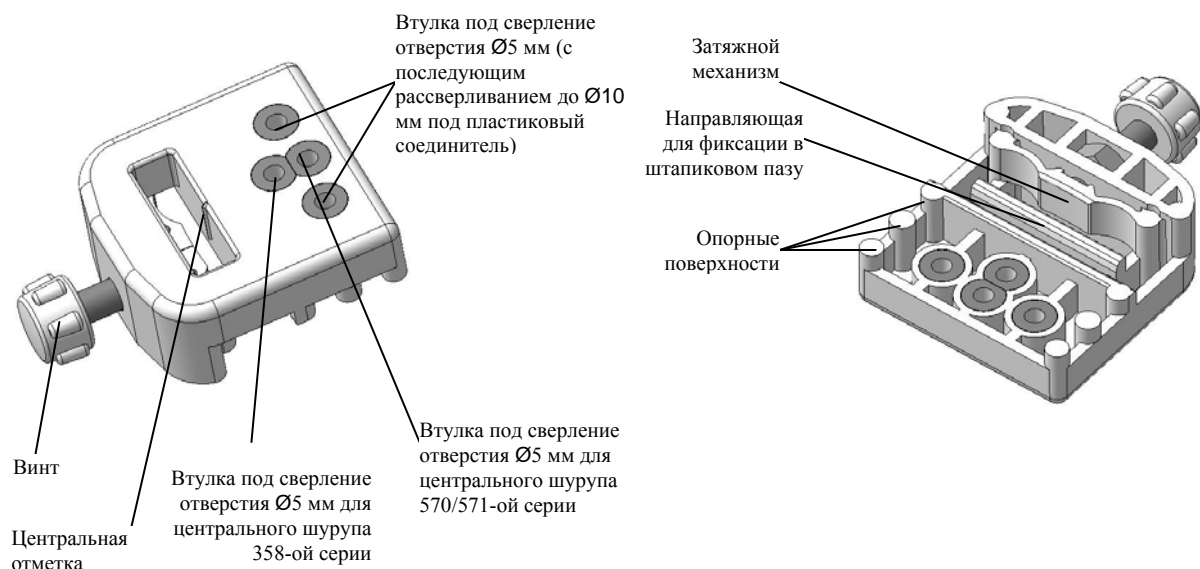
КСИ 358/570/571 Кондуктор соединителя импоста.
